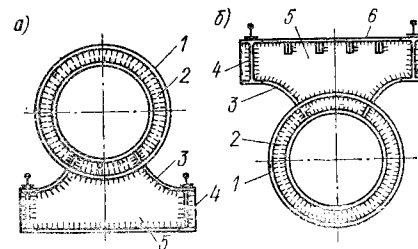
Поперечные разрезы пролетной балки перегружателей трубчато-балочной конструкции: а — перегружатель первоначальной конструкции; б — модернизированный перегружатель; 1 — главная труба; 2 — кольцевая диафрагма; 3 — гнутый настил; 4 — подрельсовая балка; 5 — поперечная балка; 6 — тормозной настил
